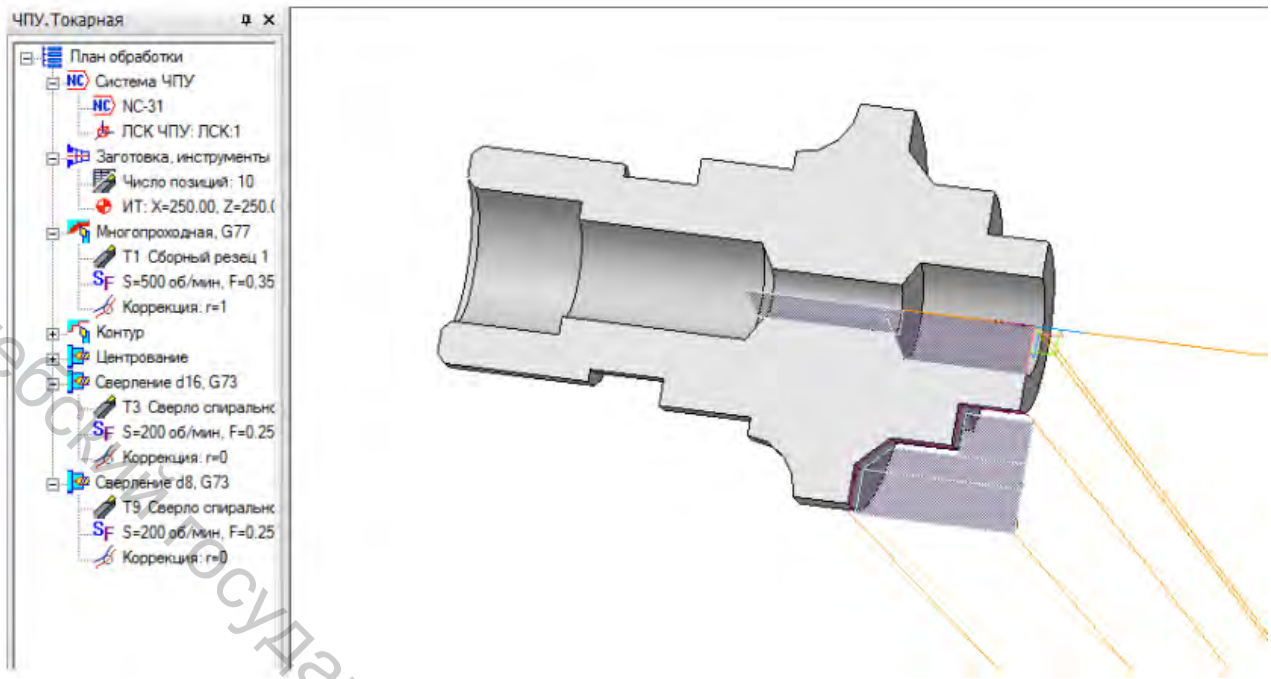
План обработки операционной заготовки для второго установка
